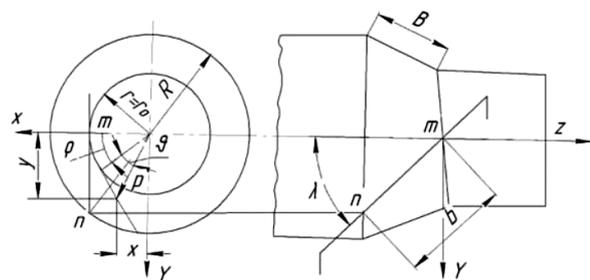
Схема продольного точения резцом с перемещаемой режущей кромкой [2]
